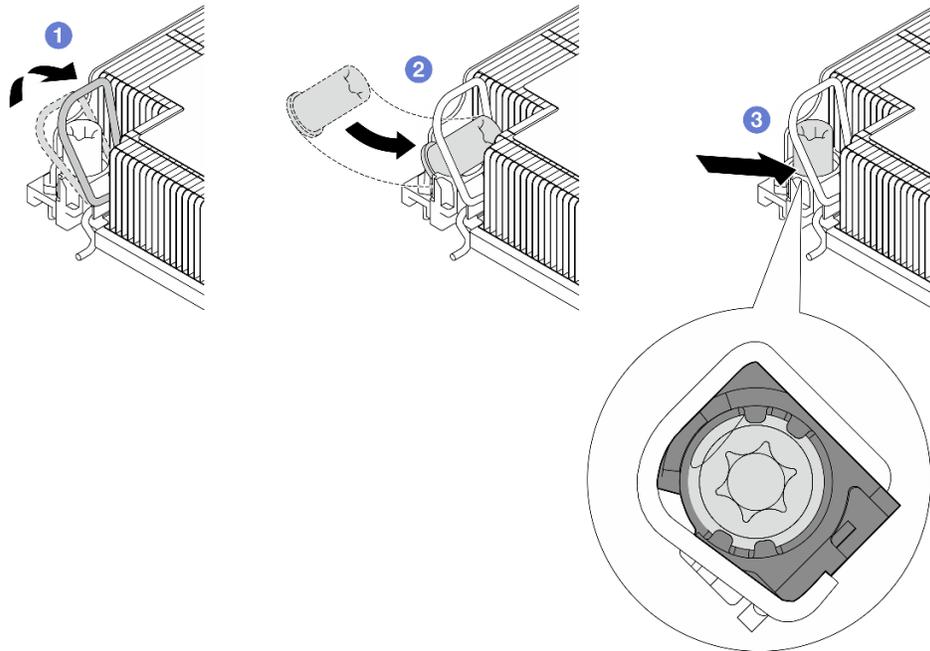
Anbringen einer T30-Torx-Mutter am Kühlkörper
